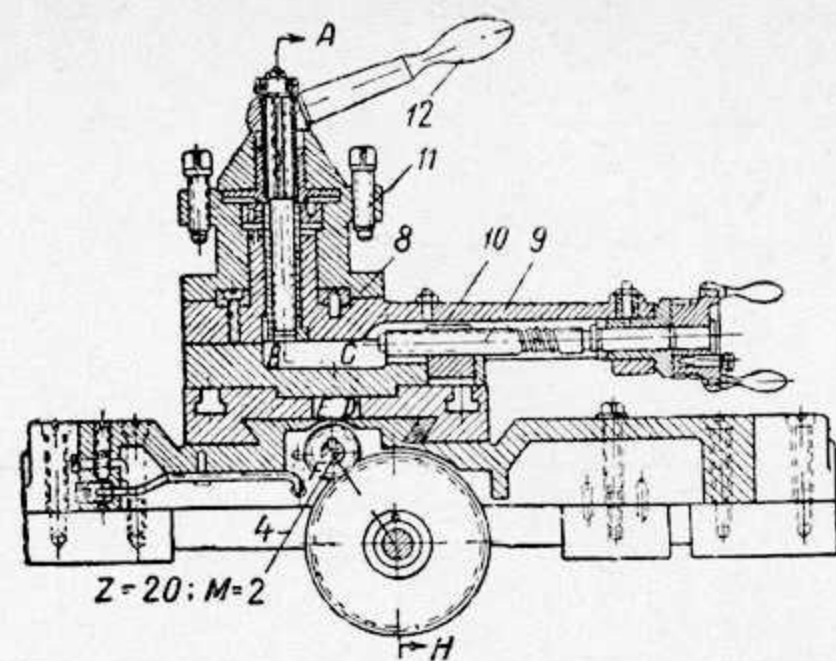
Schema sovětského universálního soustruhu obr. 419.
